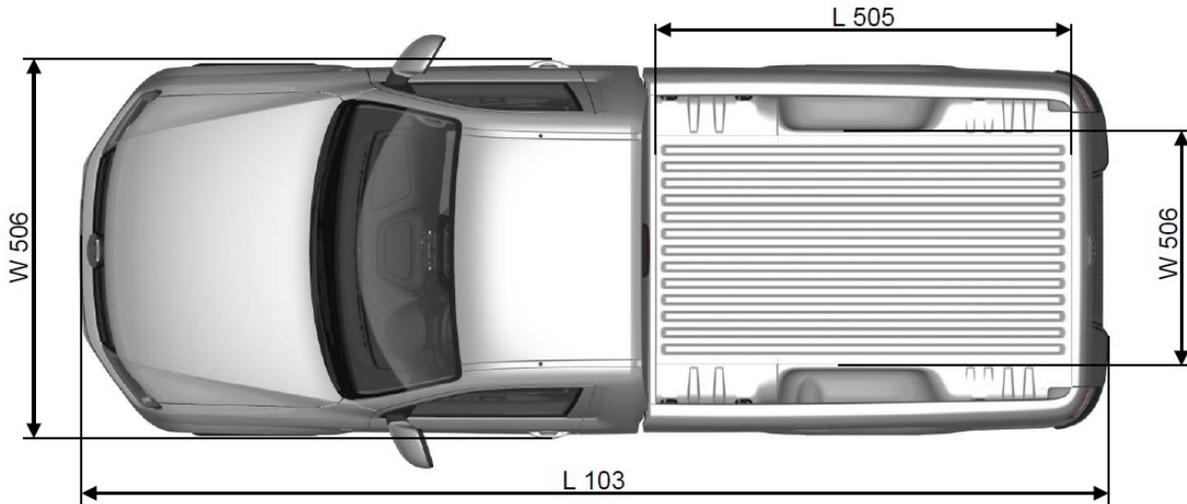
Draufsicht AMAROK-SC (Single Cab)
